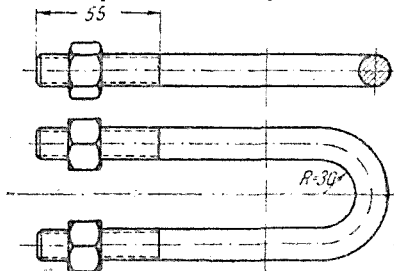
Стремянка (материал — круглая сталь 1010; длина заготовки 295 мм)
